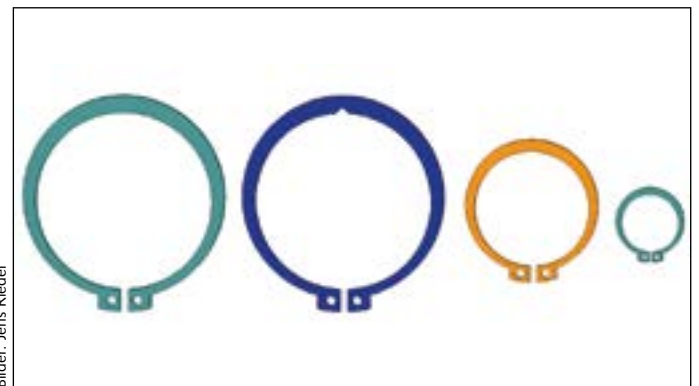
C-Ring-Probengeometrie unterschiedlicher Durchmesser (28 Millimeter, 56 Millimeter, 85 Millimeter mit und ohne Kerbe (v.r.))
